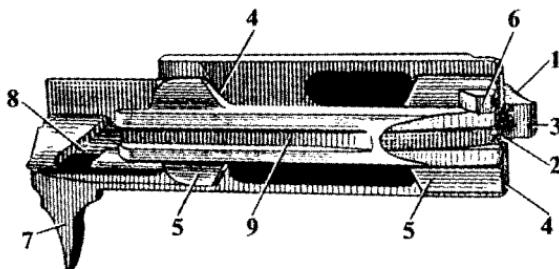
Затворная рама СВД-63: 1 — канал для возвратного механизма; 2 — канал для затвора; 3 — выступ; 4 — пазы для отгибов ствольной коробки; 5 — направляющие выступы; 6 — выступ для опускания рычага автоспуска; 7 — рукоятка перезаряжания; 8 — фигурный вырез; 9 — паз для прохода головки курка.
